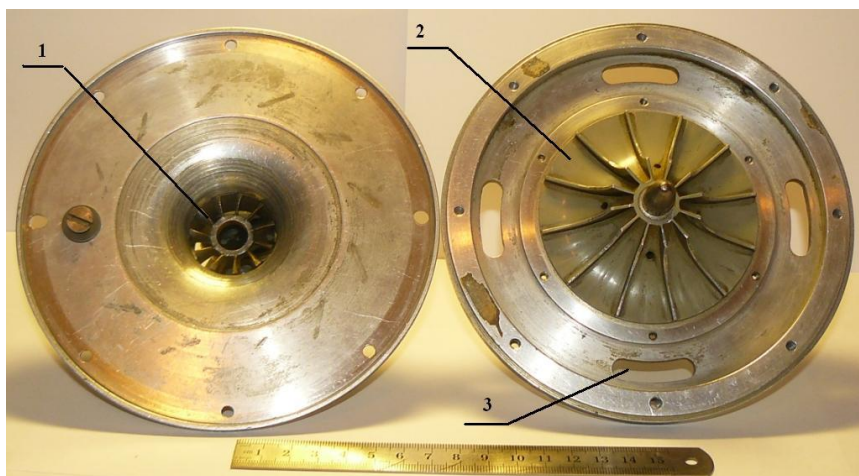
Внешний вид исследуемого центробежного компрессора:
